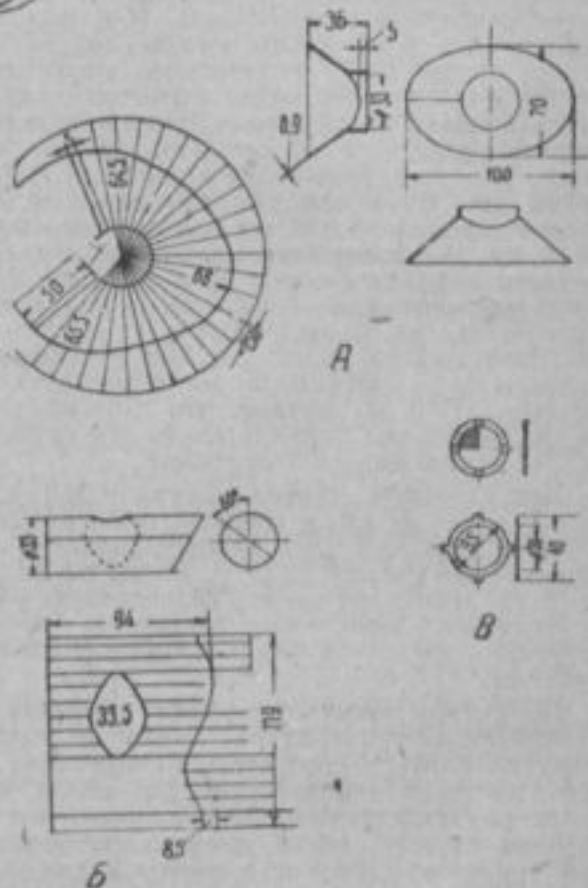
Детали газопоглотителя А — воздухоуловитель, Б — тройной патрубок, В — сетка фильтра
